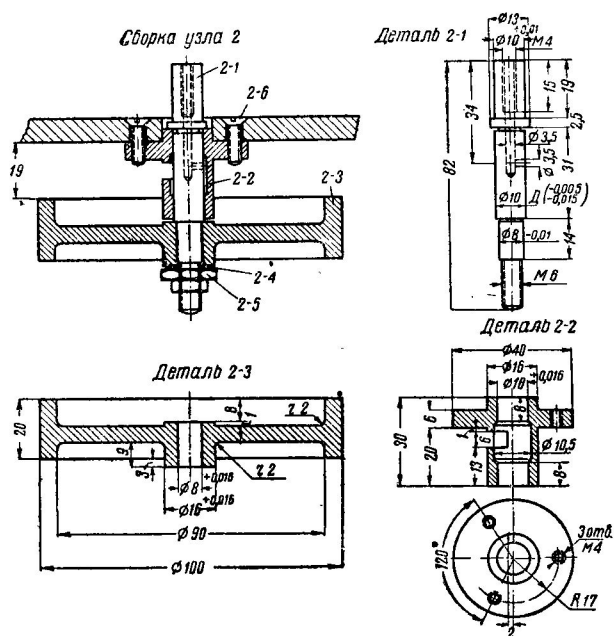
Узел 2 — перемотки пленки и его детали: 2-1 — ось (сталь 18А) — 1 шт.; 2-2 — подшипник (бронза БРОЦС6-4-3) — 1 шт.; 2-3 — колесо (сталь 3 или дюралюминий Д16Т) — 1 шт.; 2-4 — шайба 6,3 мм (сталь 3) — 1 шт.; 2-5 — гайка М-6 (сталь 3) — 2 шт.; 2-6 — винт М-4×12 мм (сталь 3) — 3 шт.
